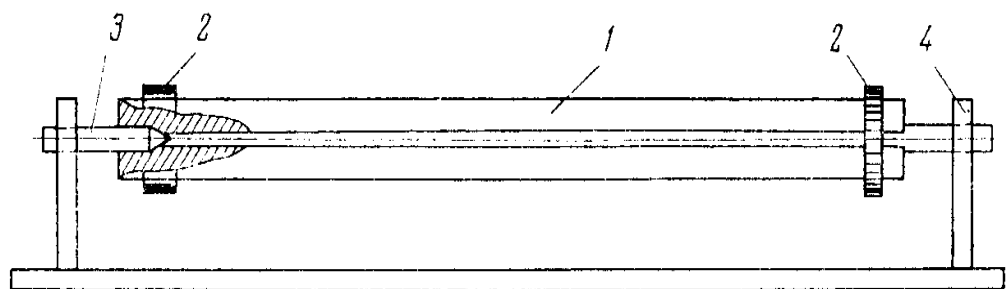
Схема болванки: 1 – циліндричний корпус (завдовжки 650 мм та діаметром 50 мм); 2 – гумові кільця; 3 – клини; 4 – стійка (підставка)
